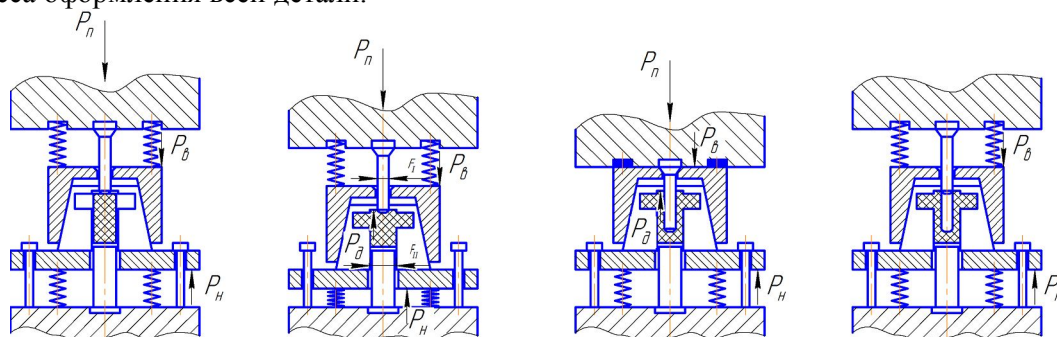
Схема штамповки деталей с применением двух буферных устройств
